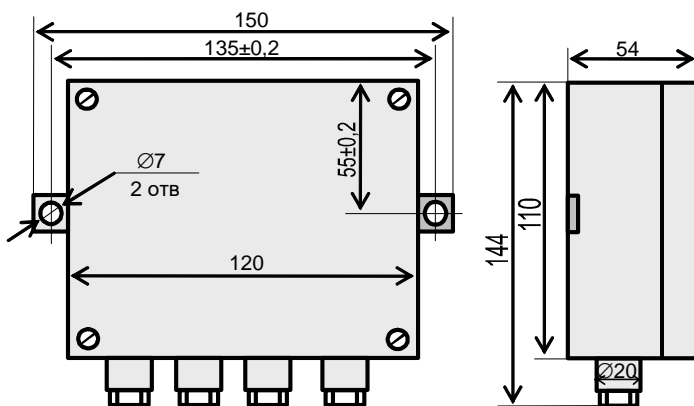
Габаритные и присоединительные размеры КБК и разветвителя
